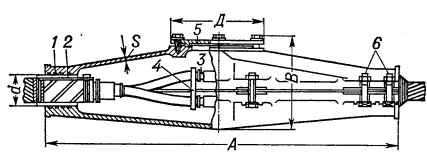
Чугунная соединительная муфта на напряжение до 1 кв: 1 — корпус; 2 — подмотка смоляной ленты; 3 — соединительная гильза; 4 — фарфоровая распорка; 5 — крышка; 6 — крепёжные болты; А, В, Д, S, d — размеры, определяющие габариты муфты.
